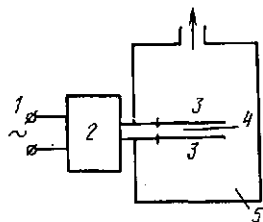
Схема сушки заготовок верха обуви токами высокой частоты
